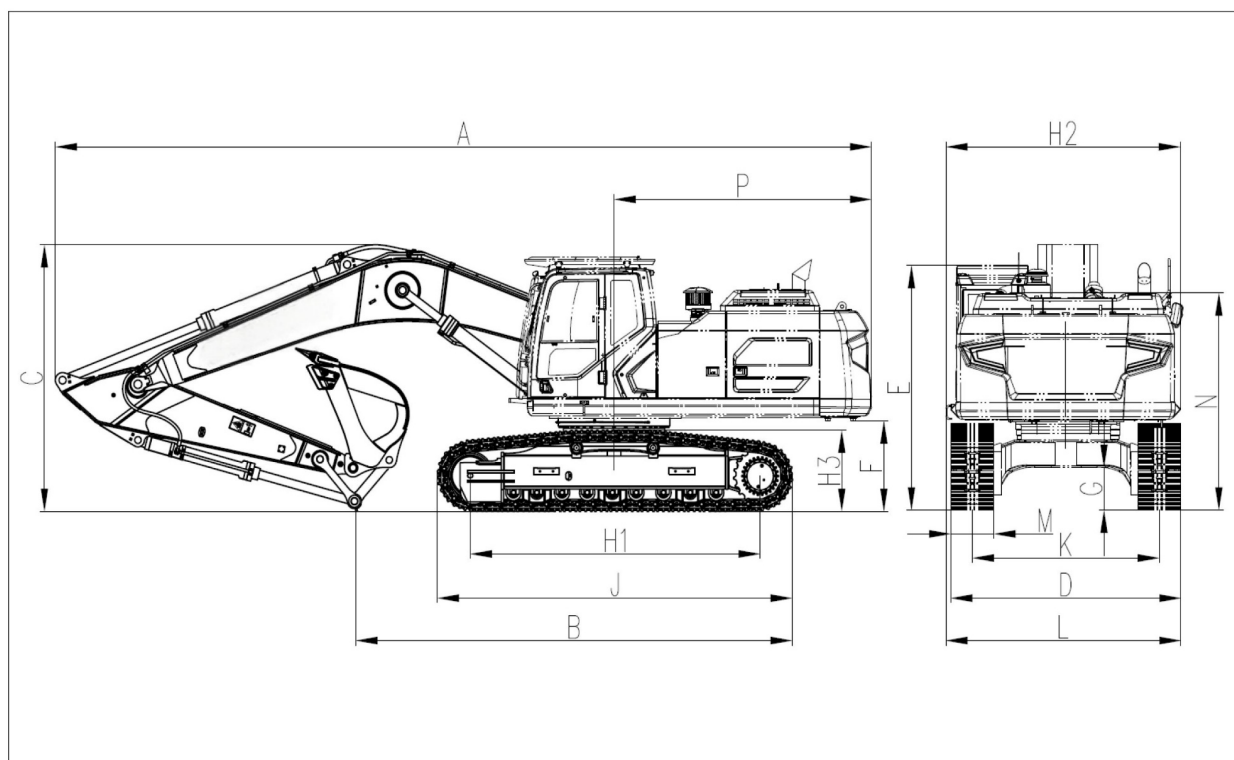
Основные размеры экскаватора в транспортном положении
